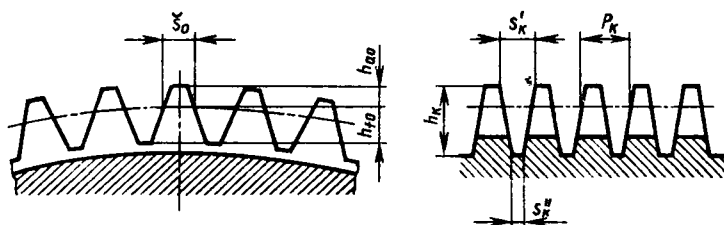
Форма припуска зубьев колес под шевингование и инструмент для их обработки
